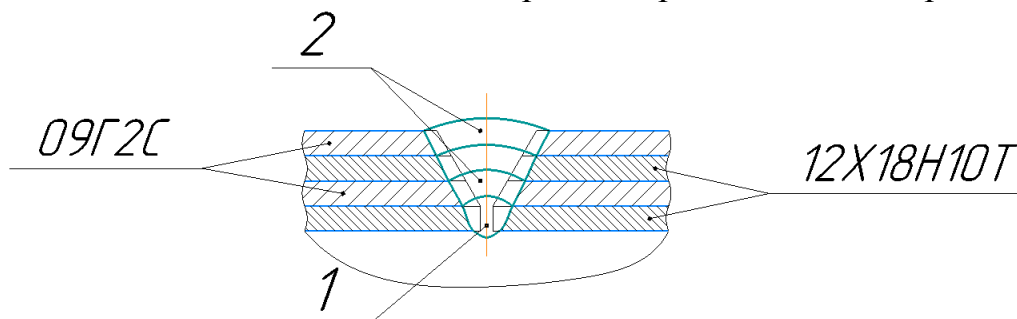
Пример одностороннего сварного соединения труб из 4-х слойного металлического материала с внутренним протектором и порядок наложения швов: 1 – корневой проход; 2 – заполняющие проходы
